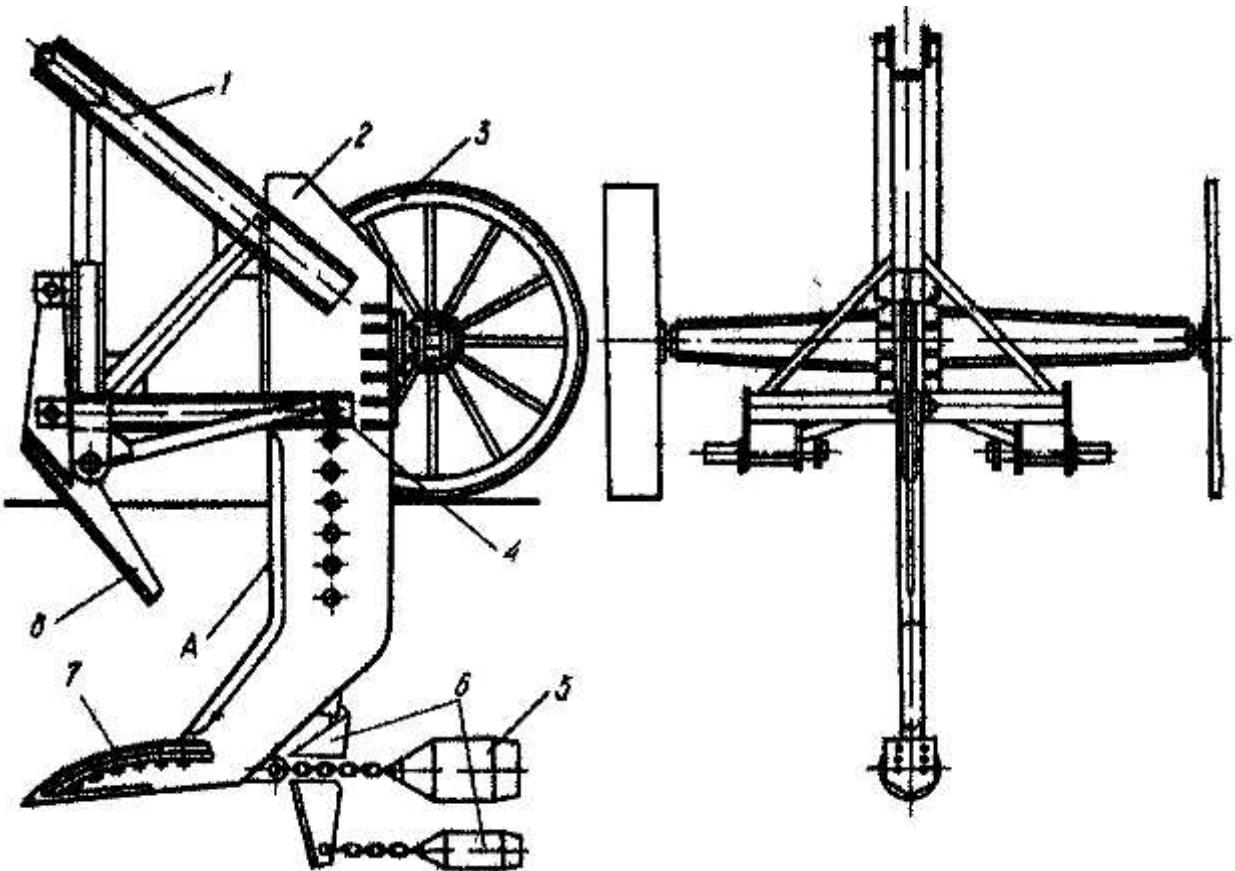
Плоскорез-глубокорыхлитель ПГ-3-100
